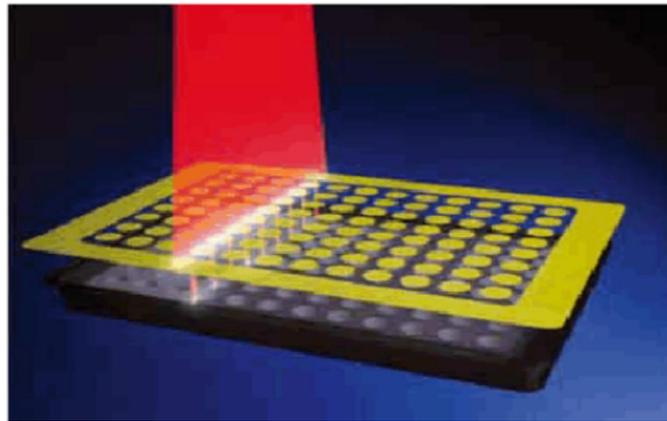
Variante 1- Maskenschweißen
